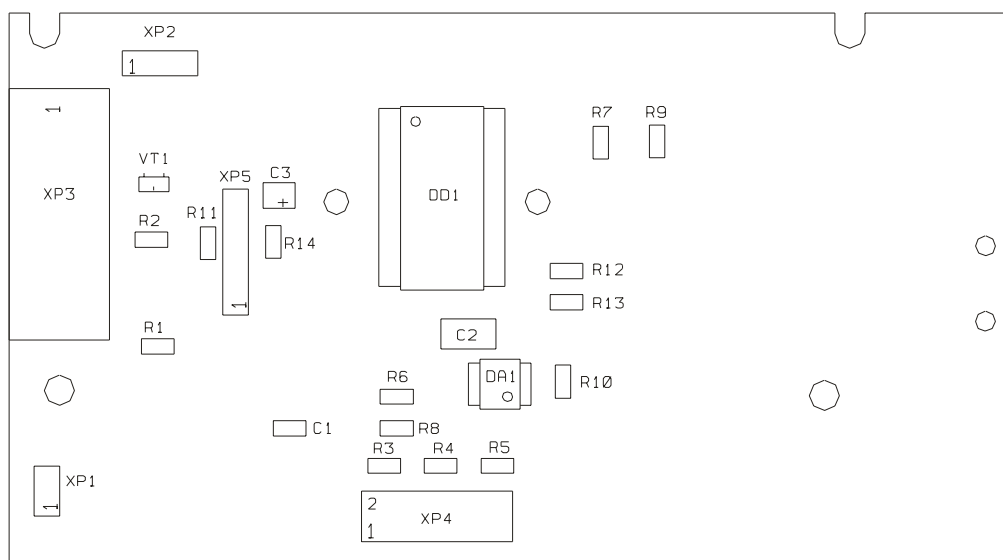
Сборочный чертеж платы обработки ТПГ-94.1. Вариант исполнения 2. Сторона монтажа.
